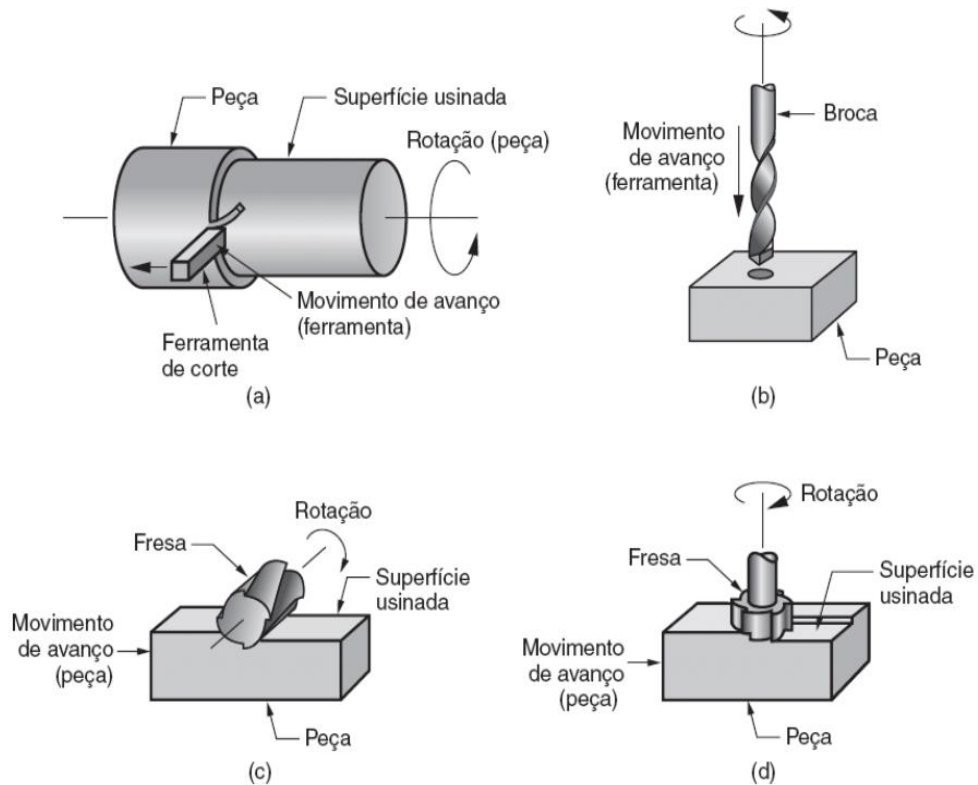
Principais processos de usinagem: (a) torneamento; (b) furação; (c) fresamento tangencial e (d) fresamento frontal ou de topo (GROOVER, 2017).
